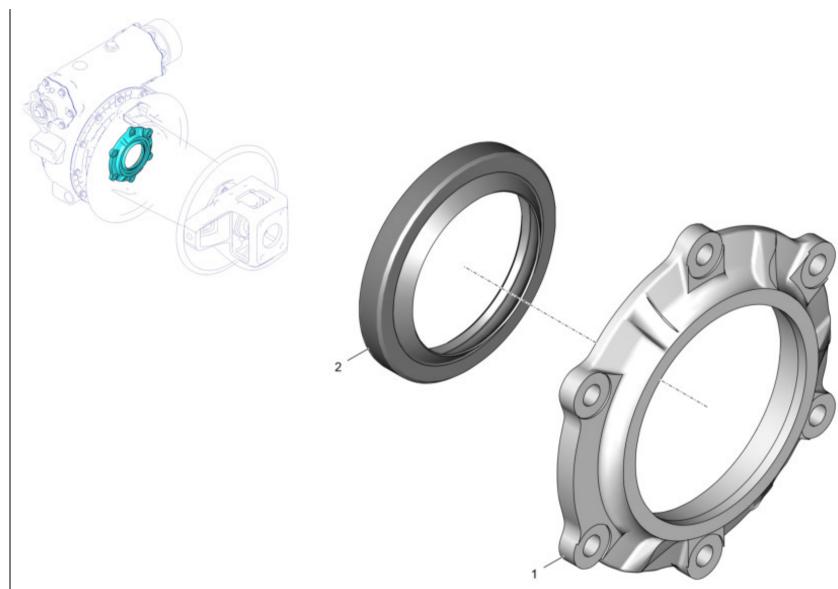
375-4501055 Крышка подшипника вала лебедки левая
